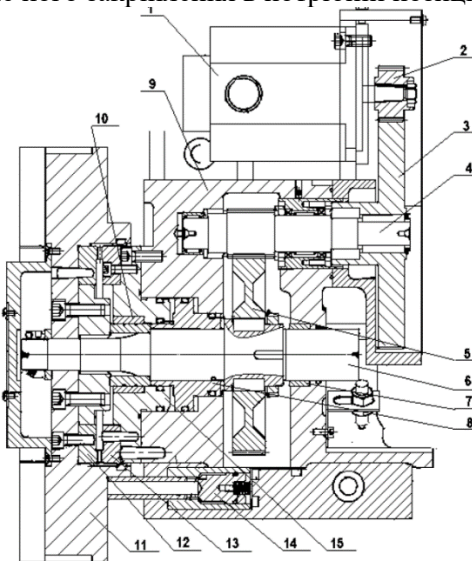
Револьверні головки токарних верстатів з ЧПК без приводу інструмента
